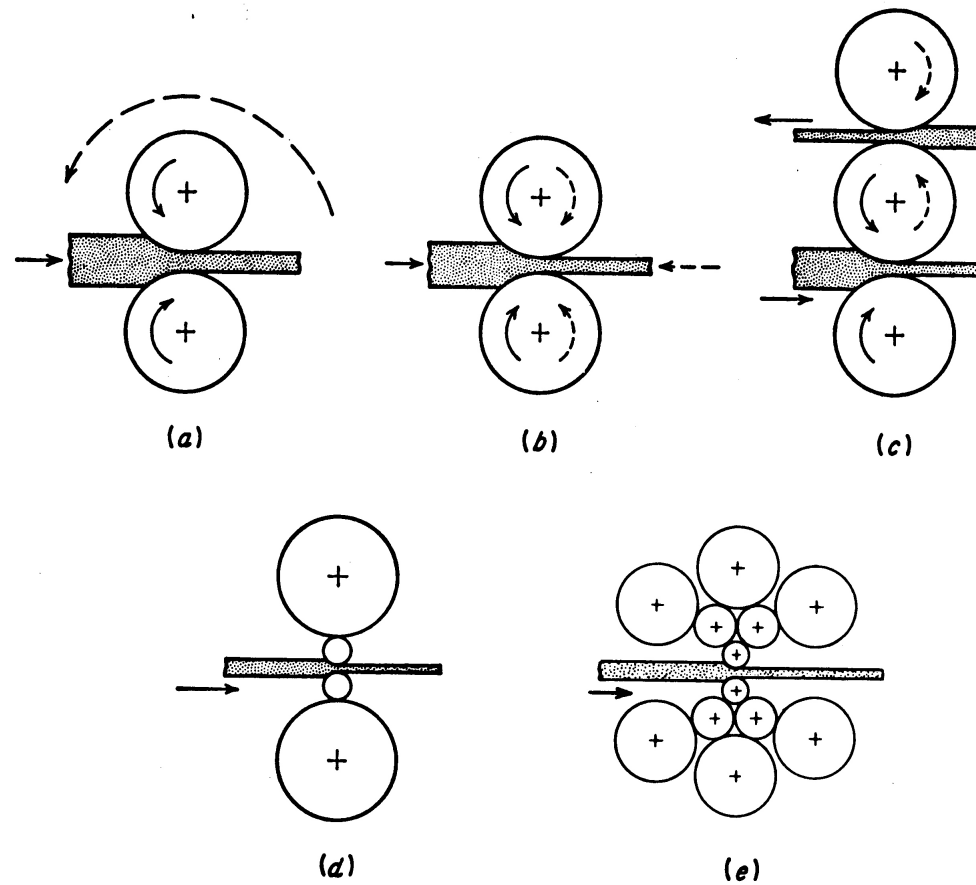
Arranjos típicos de rolos para laminadores. (a) Laminador duo; (b) laminador duo reversível; (c) laminador trio; (d) laminador quádruo; (e) laminador agrupado.
